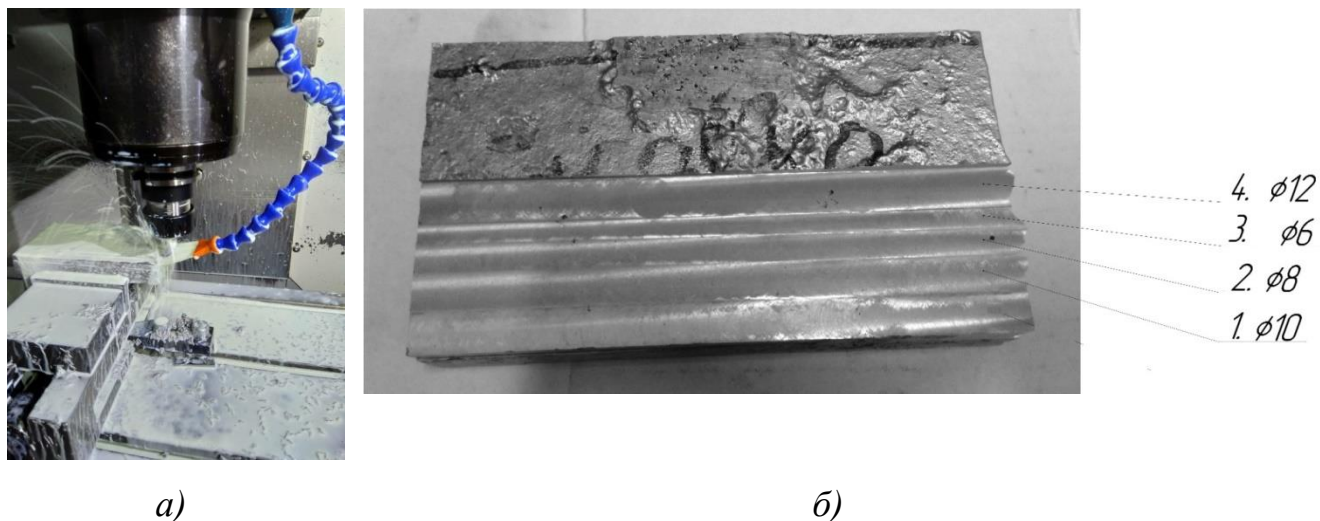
Оброблення заготовки кінцевими фрезами $\varnothing 6$ мм, $\varnothing 8$ мм, $\varnothing 10$ мм, $\varnothing 12$ мм *a)* і поверхня призматичної заготовки *б)* після обробки
